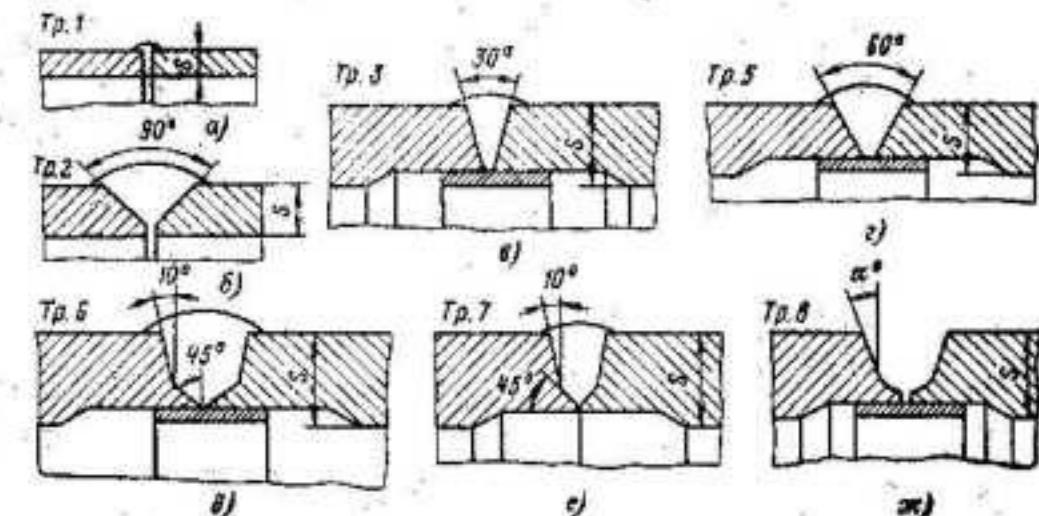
Конструкция сварных стыков для трубопроводов согласно ОСТ 24.03.005.
